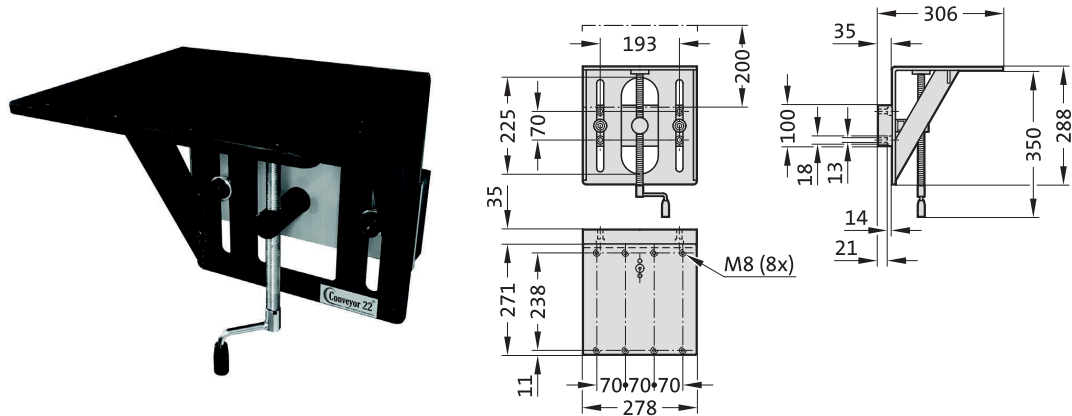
Escuadra de montaje de altura regulable para montaje del transportador
